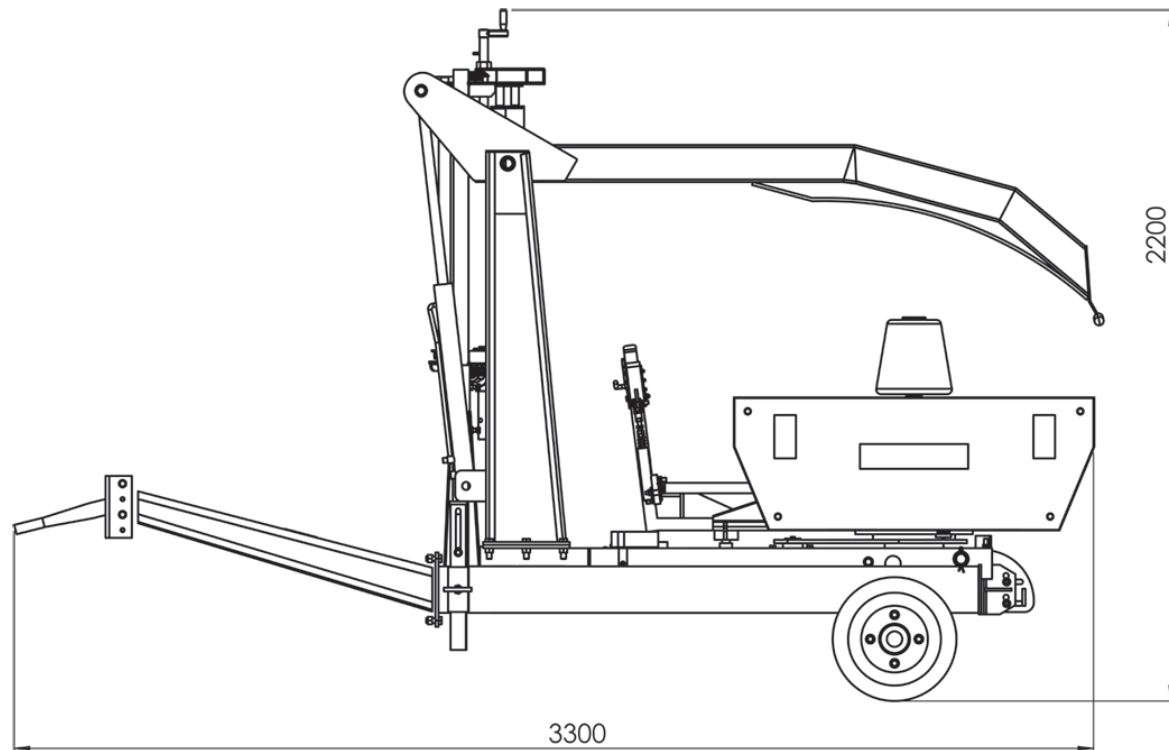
Dimensiones de la encintadora en la posición de transporte
